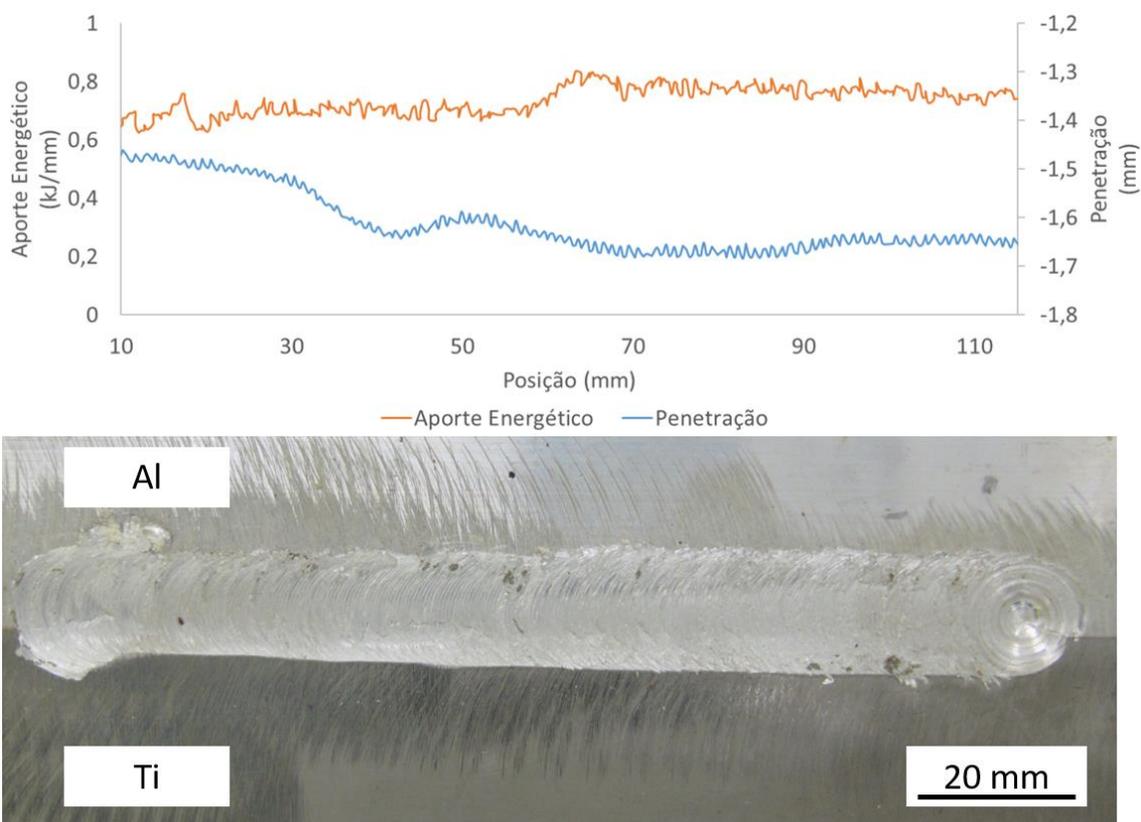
Soldagem dissimilar de AA6063-T5 com Ti6Al4V com ferramenta para chapas finas utilizando parâmetros de 300 rpm, 150 mm/min e 1,0 mm de *offset*.
